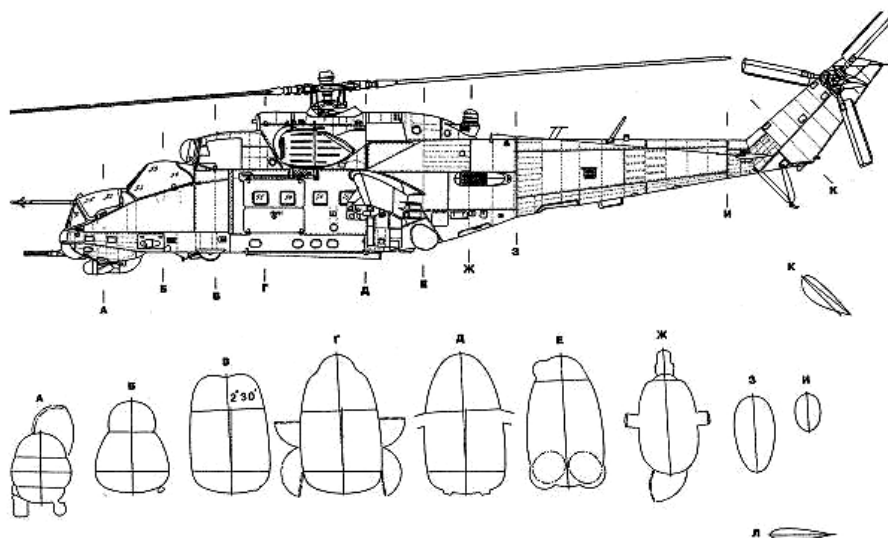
Компоновочный чертёж вертолётa с поперечными сечениями
